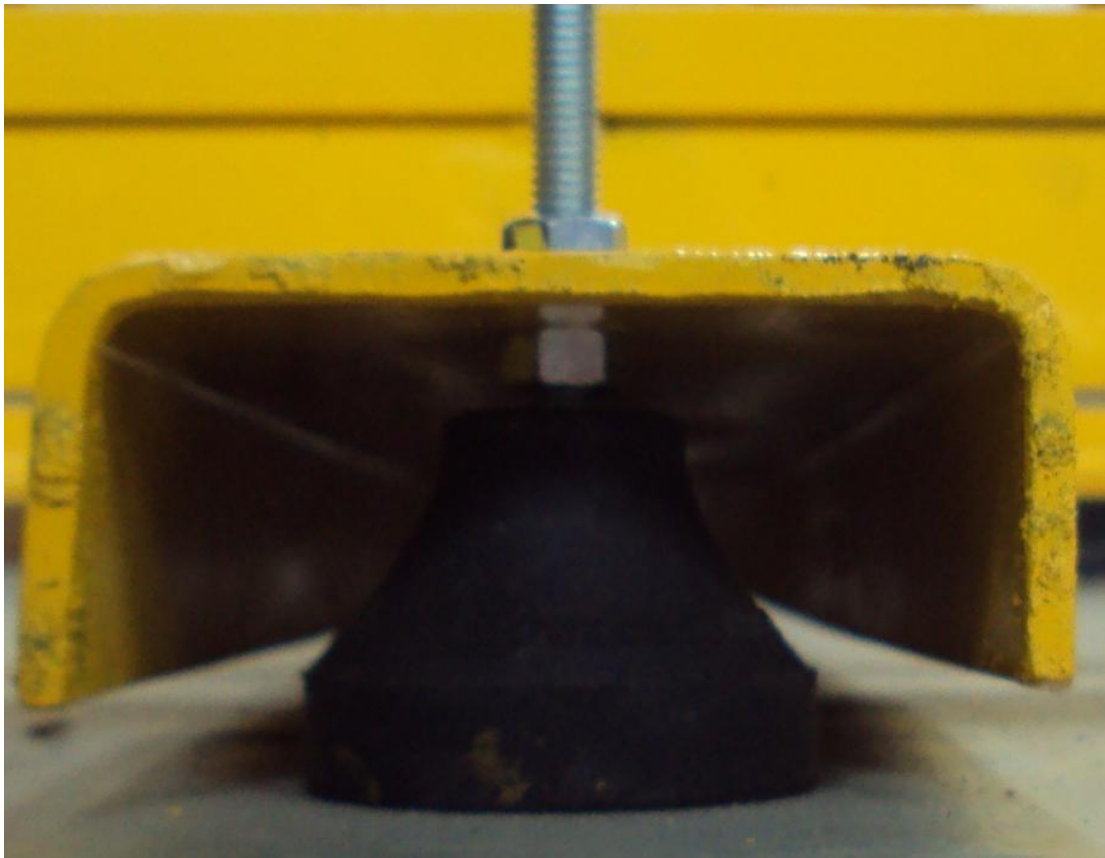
Viga com perfil em "U" e nivelador de borracha.
